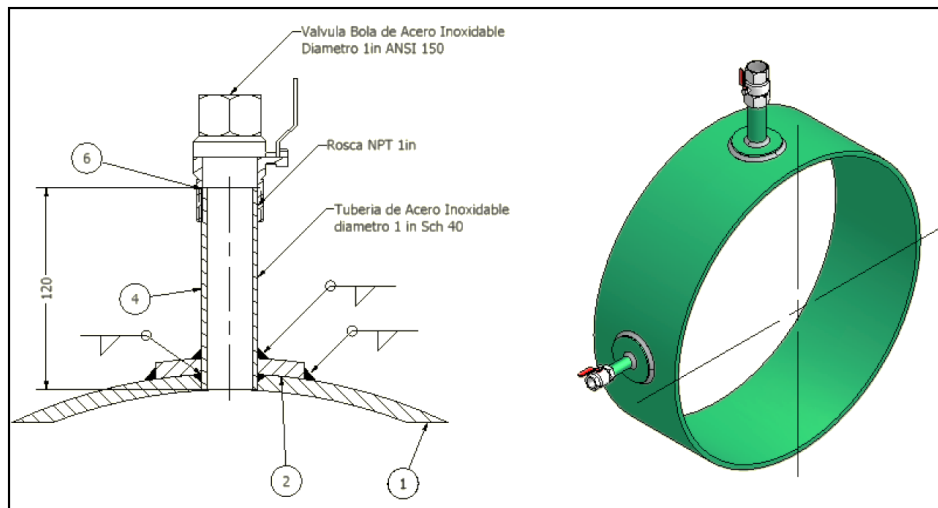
Esquema de instalación de niple con sobresano, no se debe aplicar soldadura al interior de tubo.
